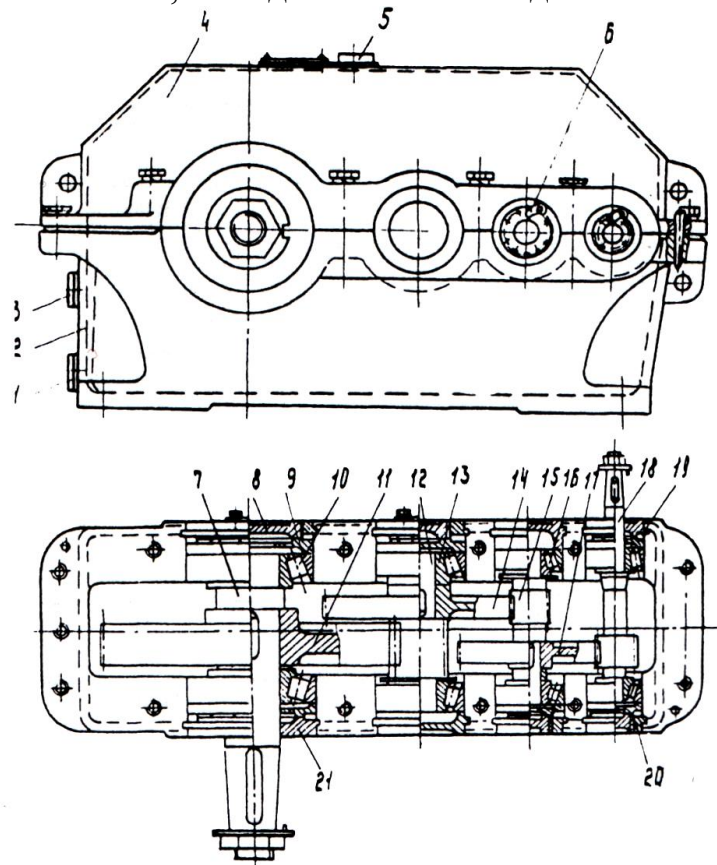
П7 Общий вид редукторов типа 1ЦЗУ
